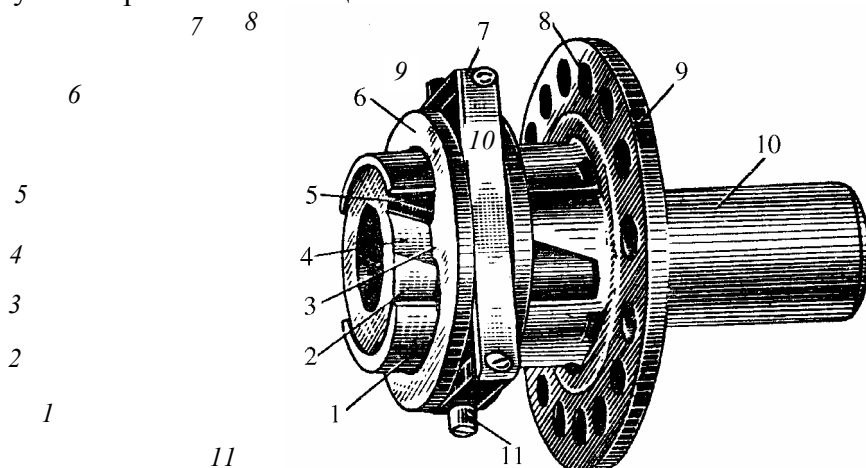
Приспособление для изменения угла опережения начала впрыска топлива:
